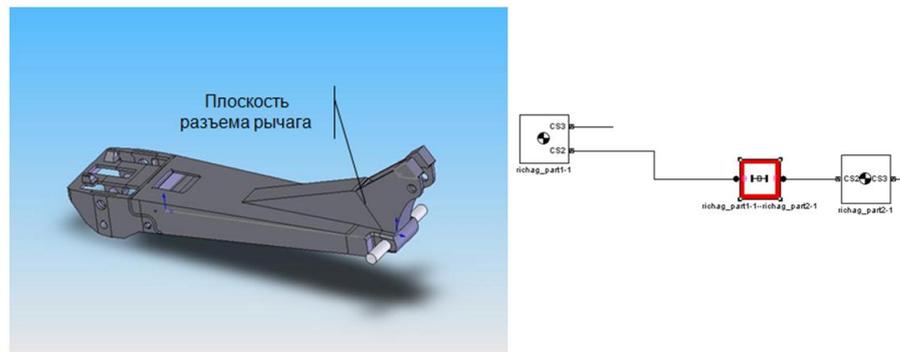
Подготовка *CAD*-модели рычага для обеспечения упругости и вид модели в *SIMMECHANICS
